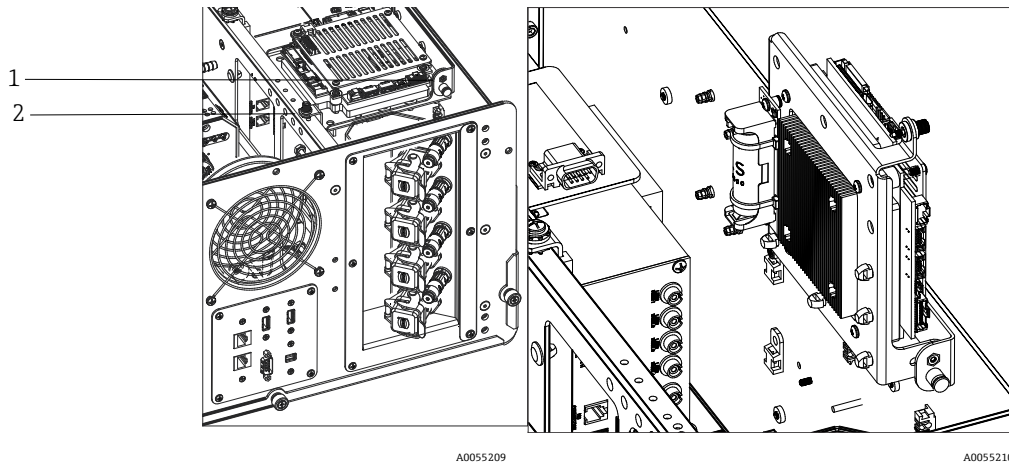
Vue d'ensemble arrière avec plaque de contrôleur en position ouverte
